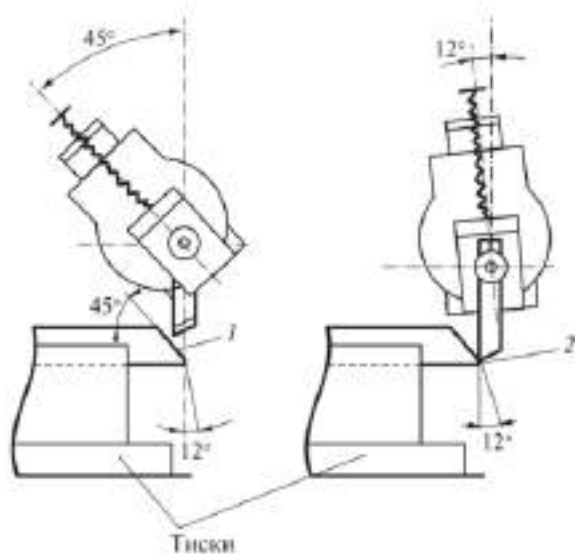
Схема строгания скосов на заготовках для резцовых державок
